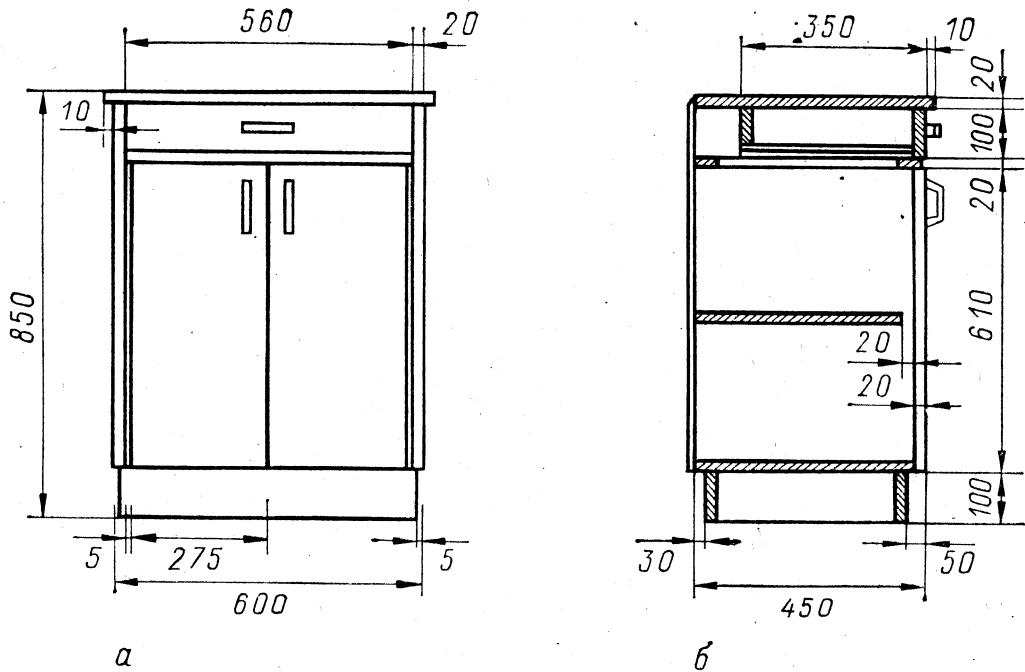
Эскиз разделочного стола-шкафа: а — вид спереди; б — поперечный разрез
